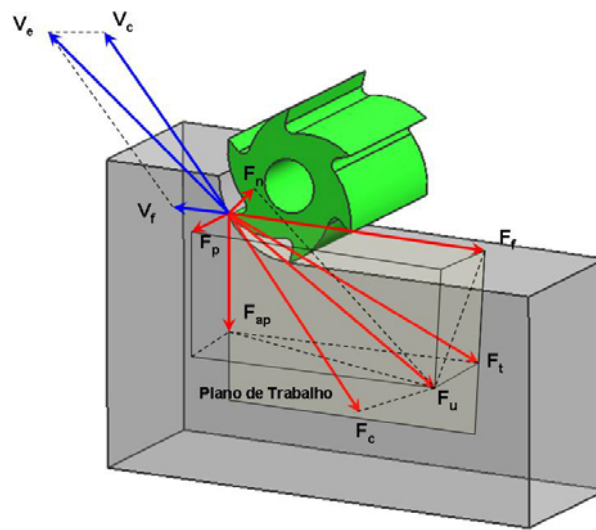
Força de usinagem e suas componentes no fresamento [67, 68].
